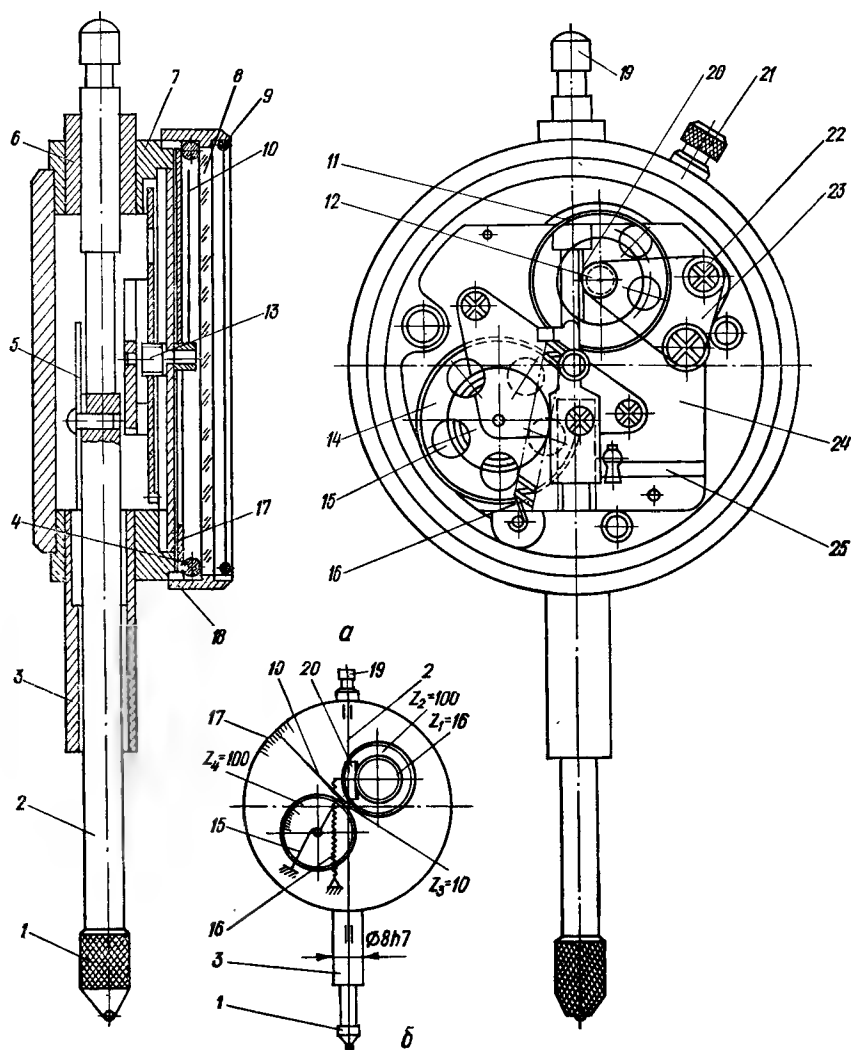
Конструкция (а) и кинематическая схема (б) индикатора часового типа.
